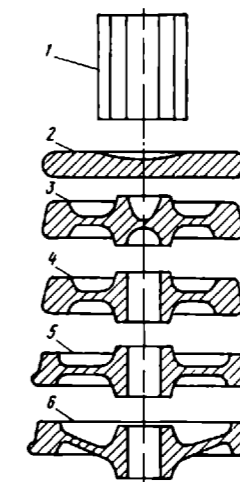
схема деформации заготовок на заводе фирмы Bonatrans: 1 – заготовка; 2 – осадка; 3 – штамповка; 4 – прошивка отверстия; 5 – прокатка; 6 – выгибка диска и калибровка
